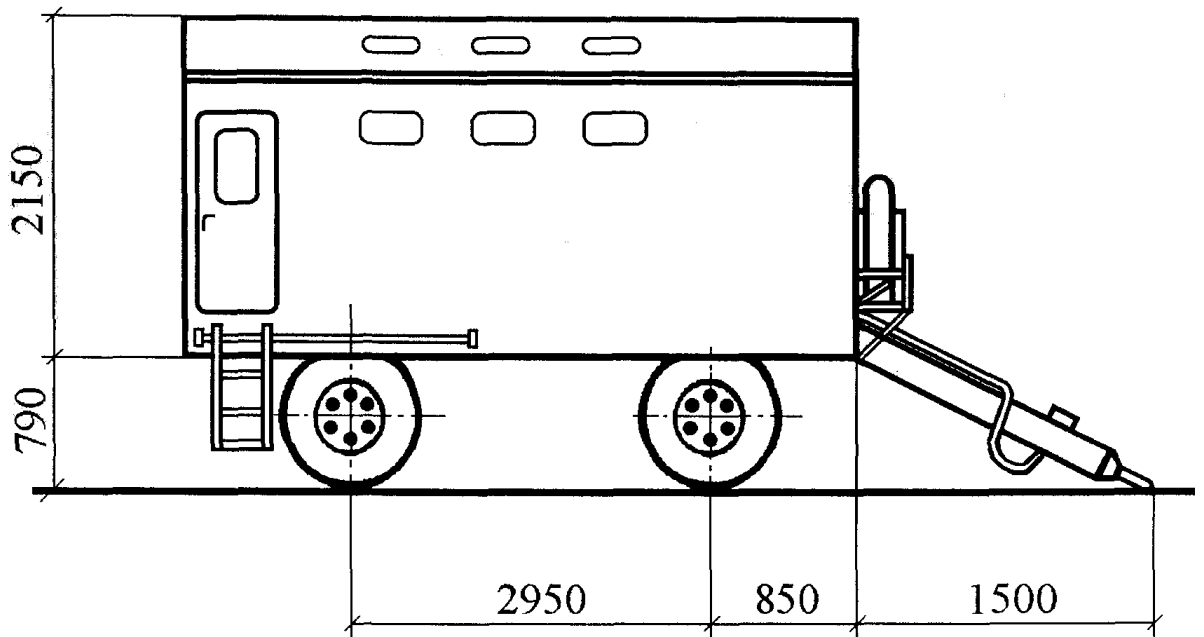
Передвижное караульное помещение на базе домика ЛВ-56
